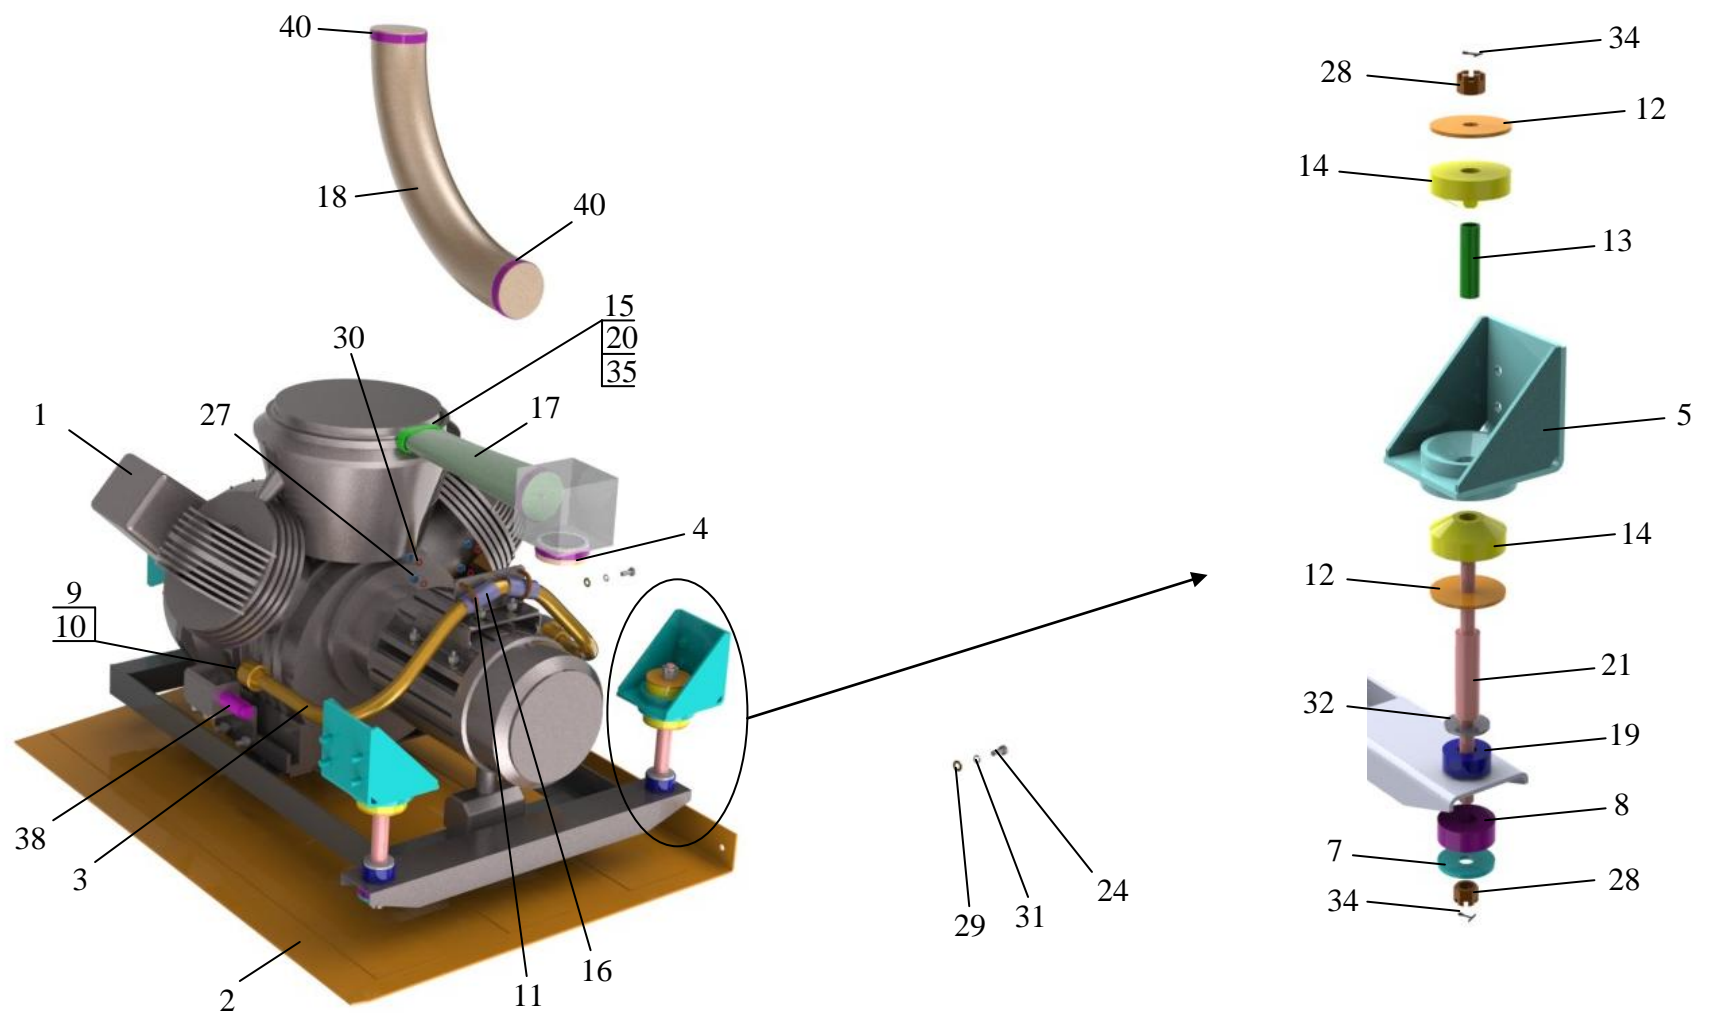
Установка компрессора АКСМ 333-231300.000
